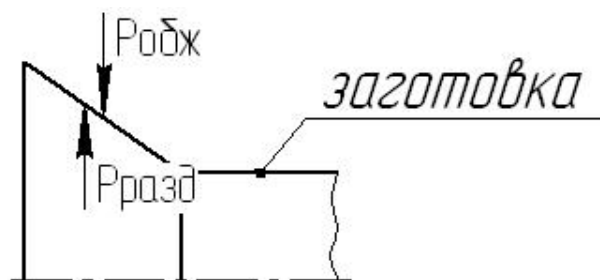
Схема нагружения заготовки в начале первого перехода профилирования из конической заготовки
